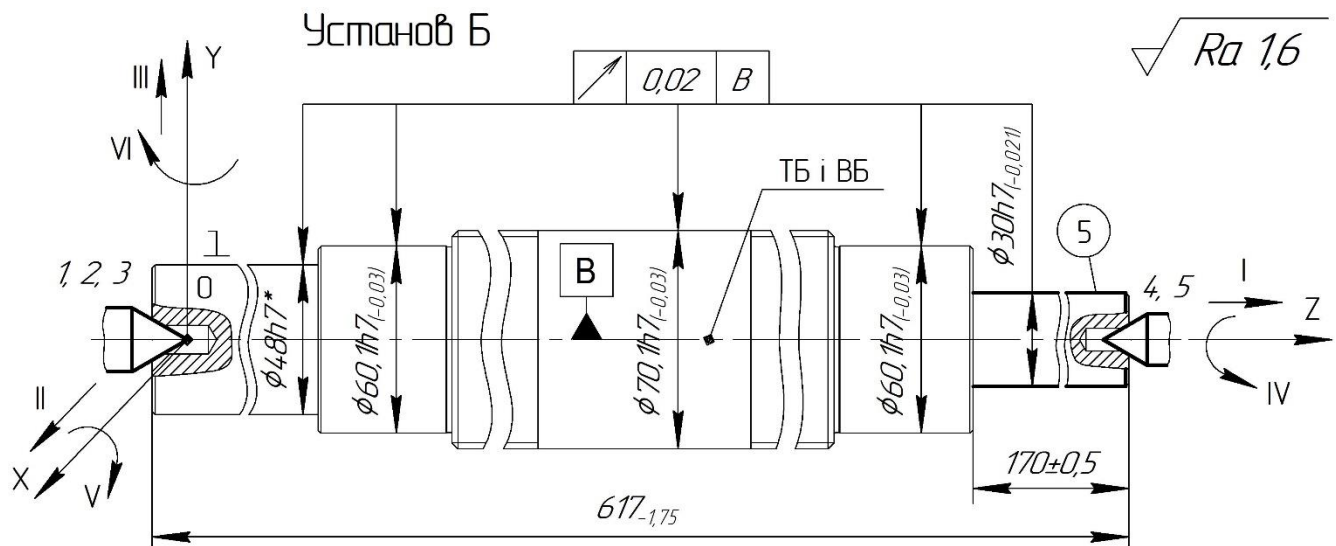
Ескіз заготовки на операції 040. Установ Б
